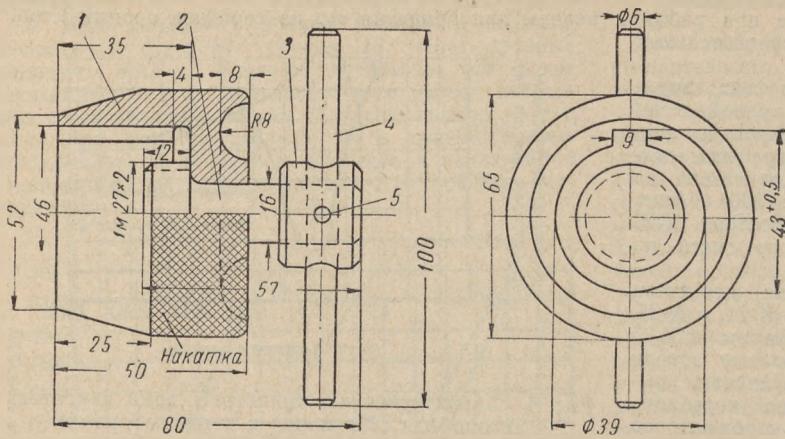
Общий вид приспособления для центровки крышки распределительных шестерен двигателей ГАЗ-51 и „Победа“.
